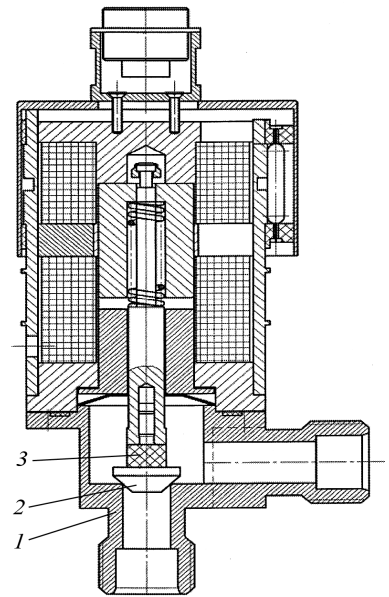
Конструктивна схема експериментального зразка клапана з жорстким ущільненням запірного вузла типу «метал–метал»: 1 – сталевий затвор; 2 – сталевий корпус з сидлом; 3 – демпфувальний елемент
